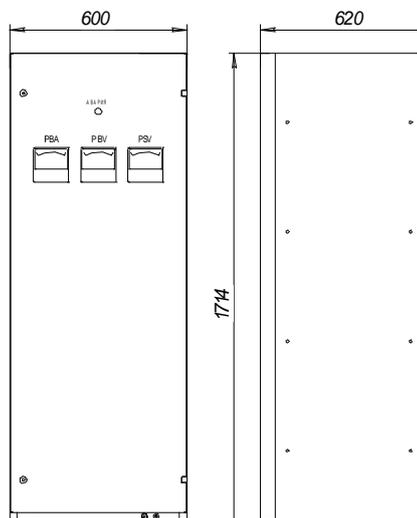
Габаритный чертеж УЭП-АО
